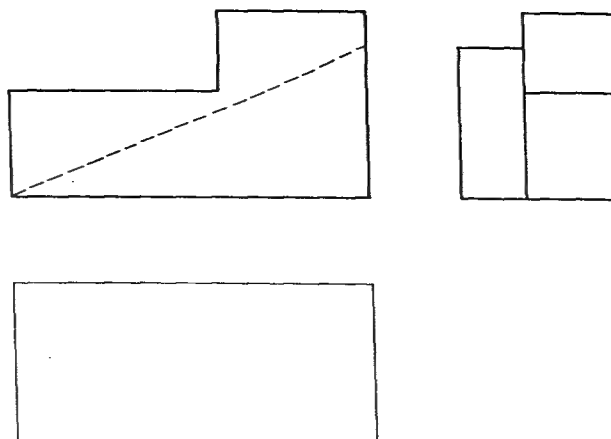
Dibujar la planta del objeto representado mediante alzado y perfil.
